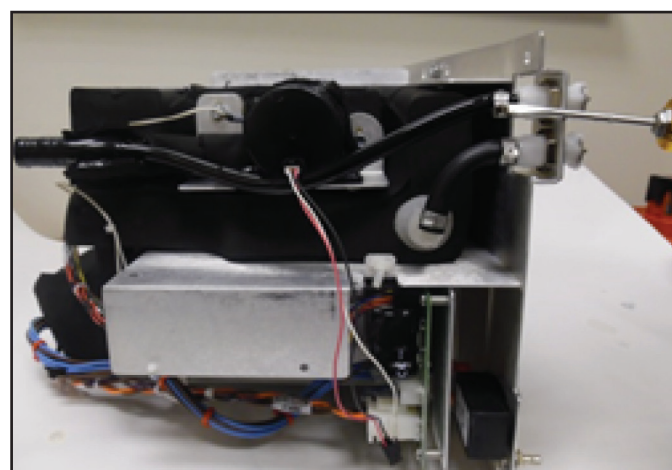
Desserrage du collier de serrage (étape 3)
